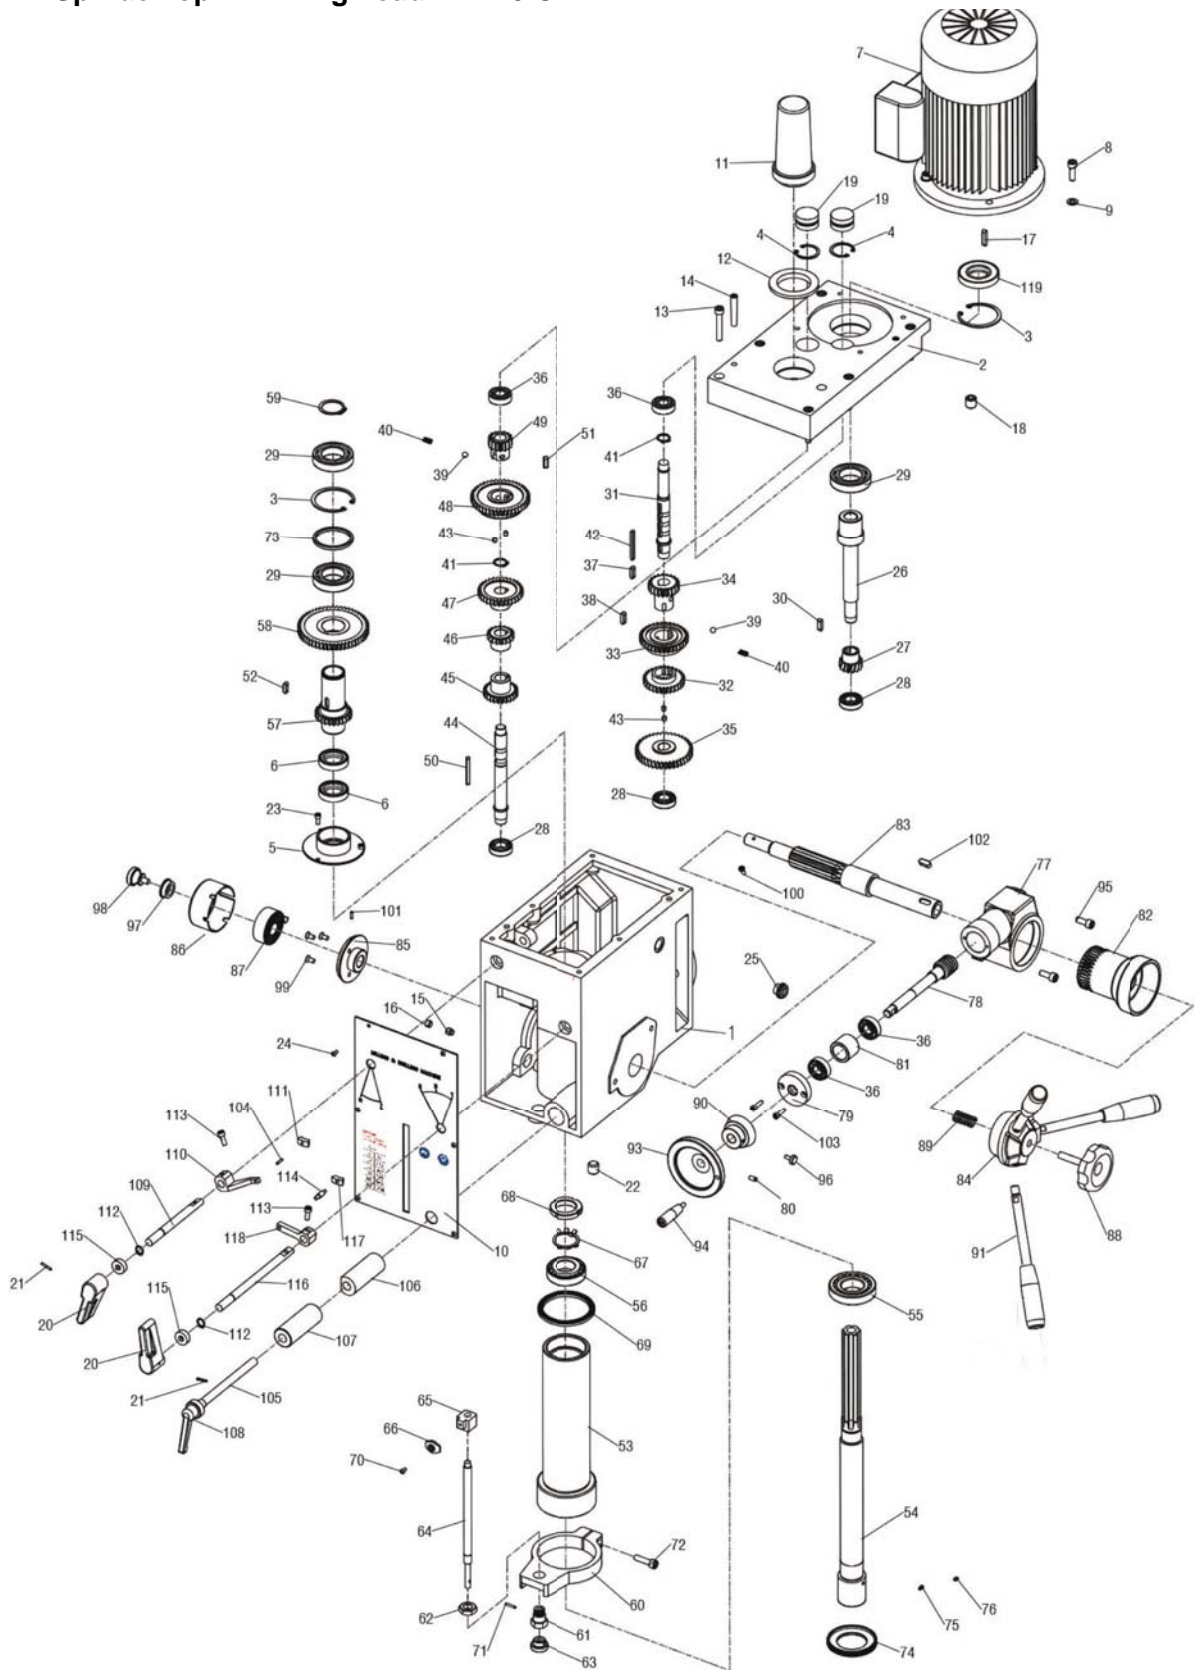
Spindelkopf - Drilling head - DH40 CT
